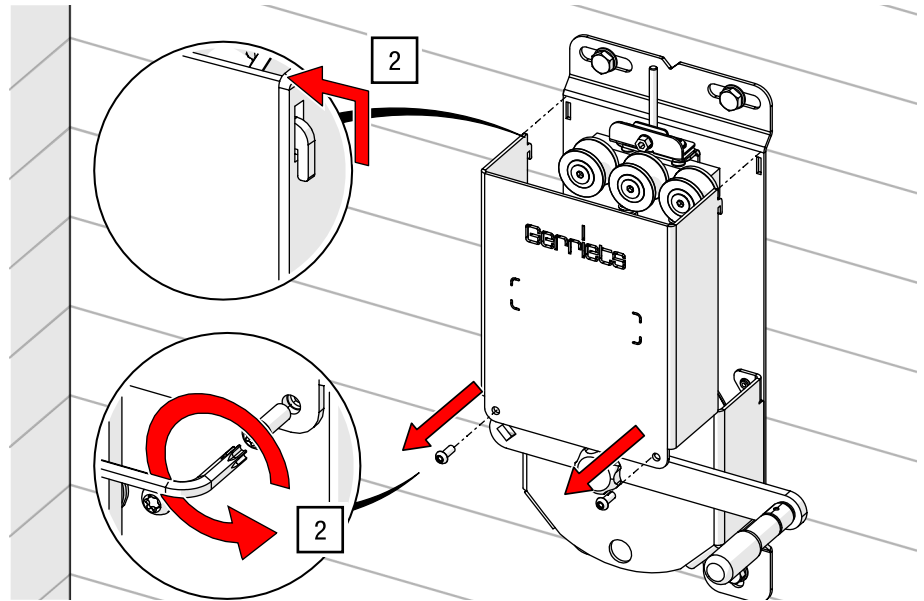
Gehäuseschrauben lösen und Gehäuse öffnen
